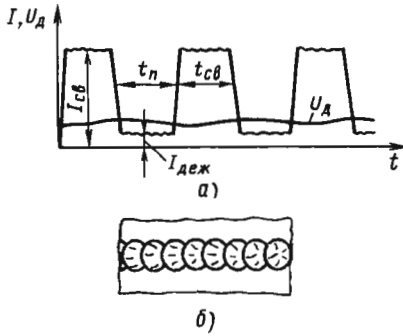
Форма импульсов тока (а) и вид шва (б) при импульсно-дуговой сварке
